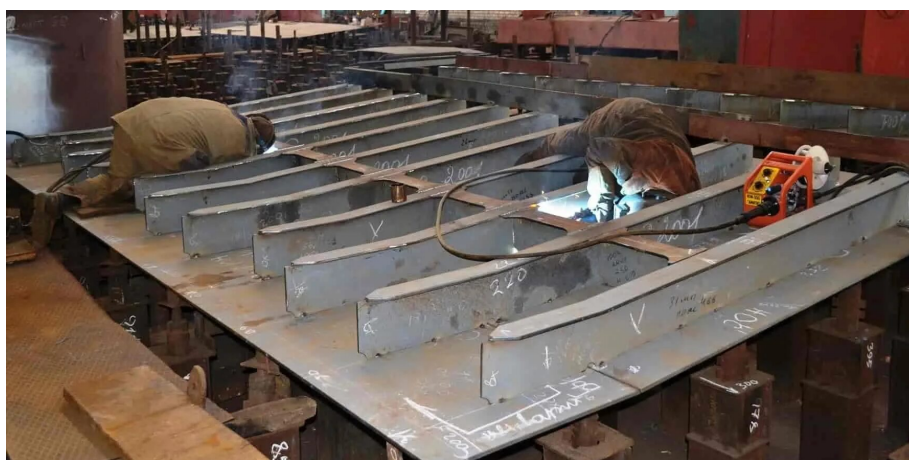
Выполнение сварных швов с применением механизированной сварки в защитных газах при изготовлении судовых секций
